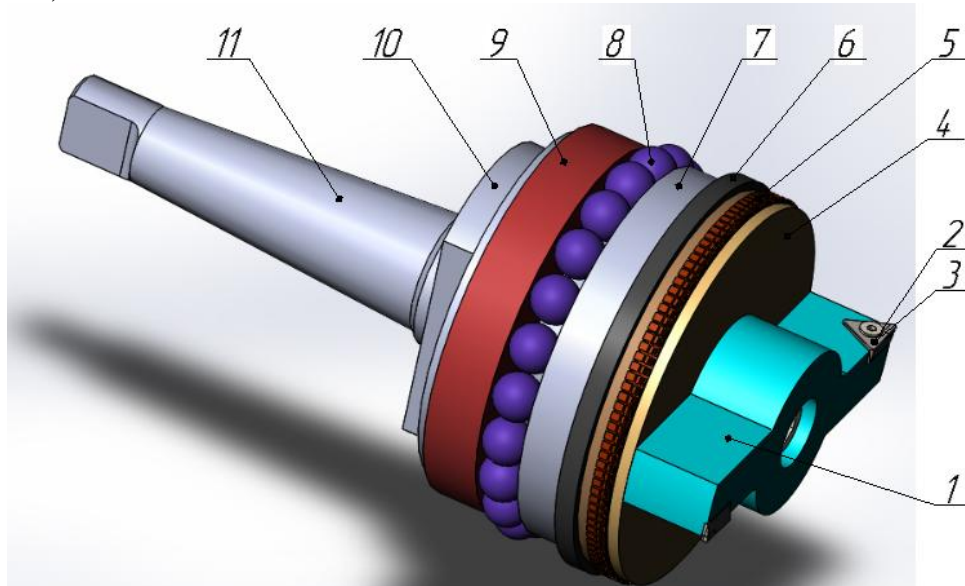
3D-модель магнитно-динамического инструмента для совмещенной обработки: 1 – расточная головка; 2 – режущая пластина; 3 – винт; 4 – уплотняющее кольцо; 5 – щетка; 6 – фетровая втулка; 7 – щетка; 8 – деформирующий элемент; 9 – магнитная система; 10 – гайка; 11 – конус Морзе
